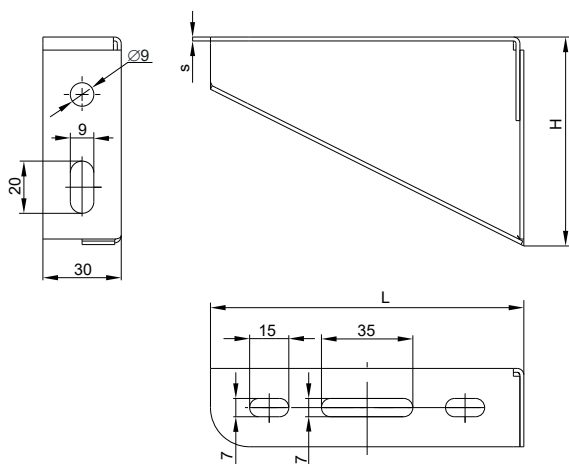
Кронштейн настенный / Figure B.1 – Wall bracket
